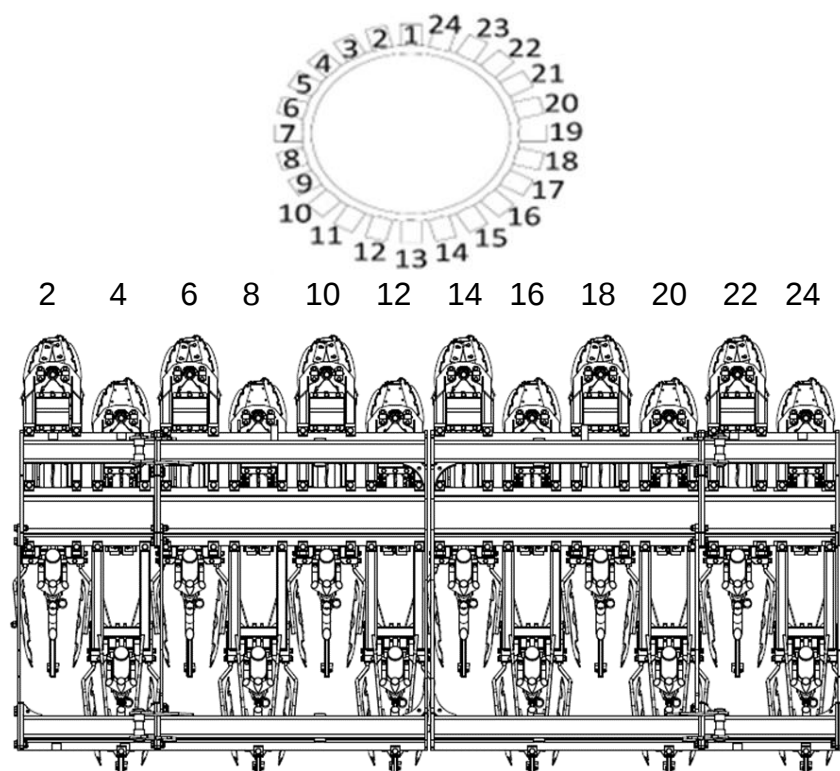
Schemat ułożenia węży ST600 16 ramek
